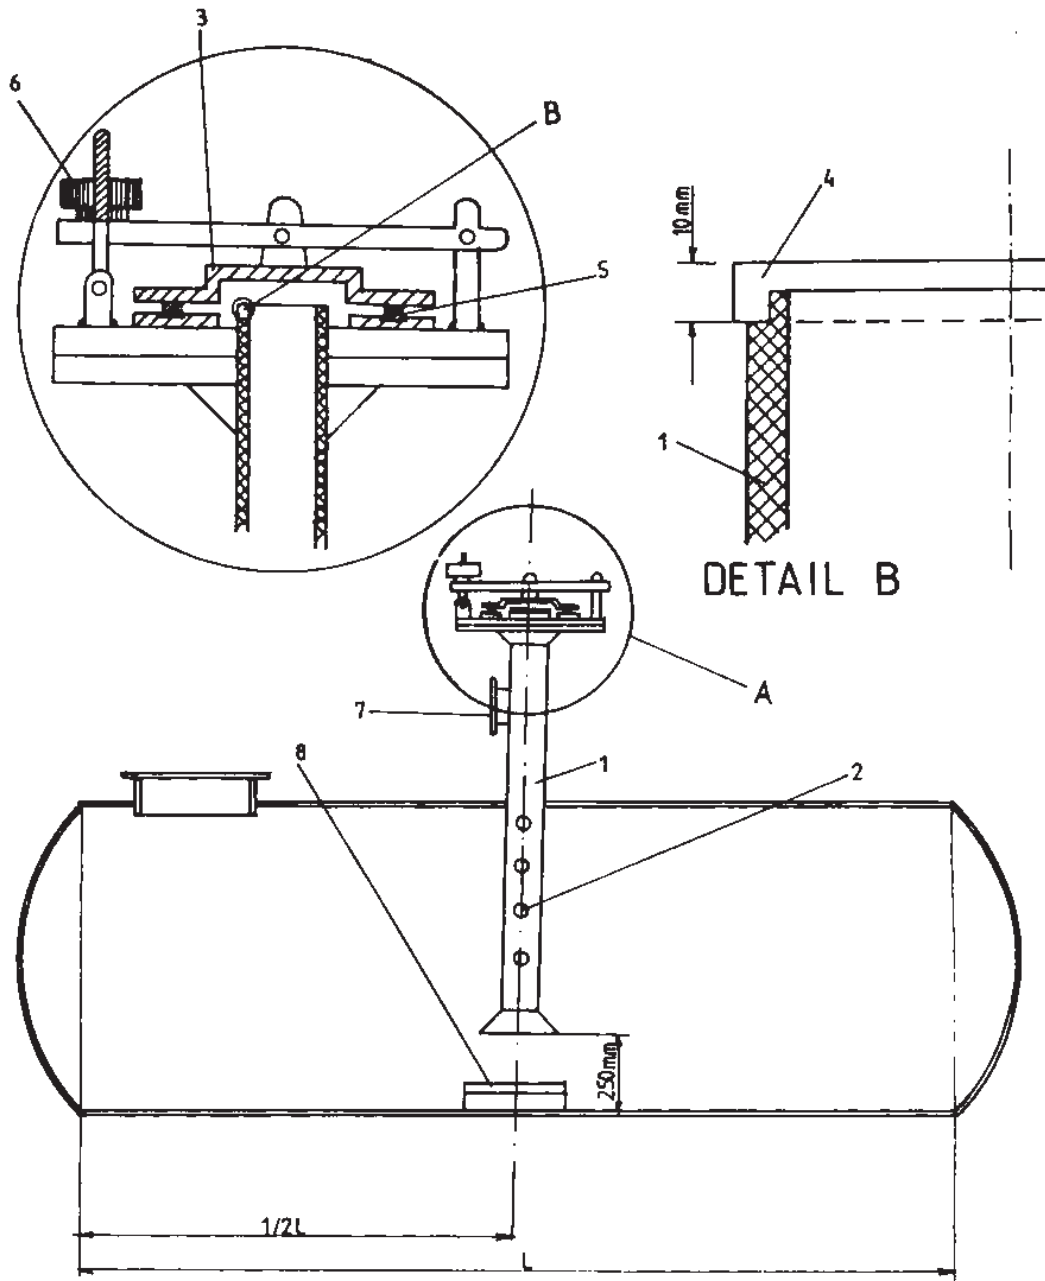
Detalles del diseño del tubo guía en un tanque cilíndrico horizontal.
